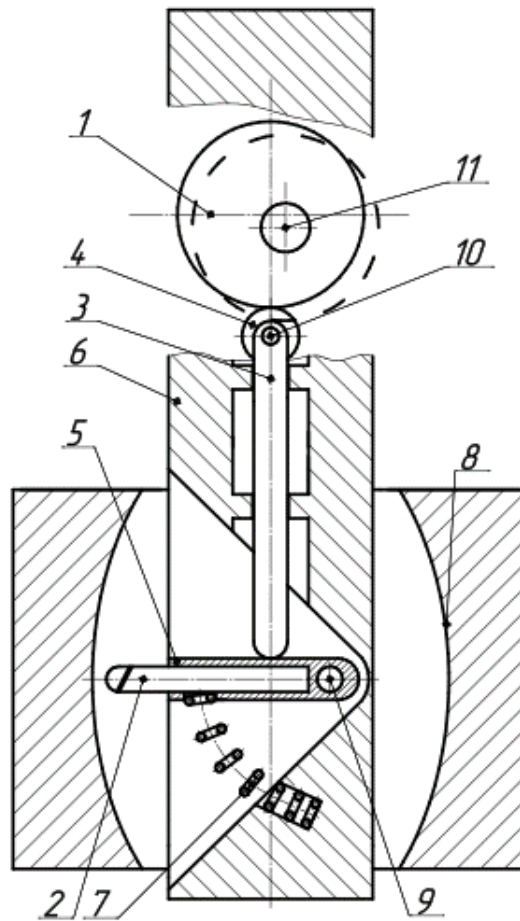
Пристосування для обробки еліпсоїда обертання:
